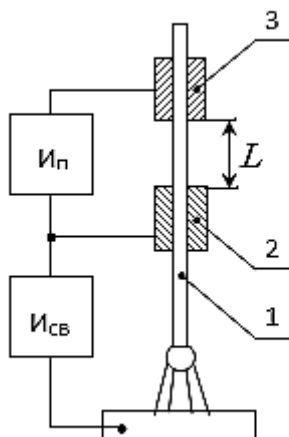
Схема предварительного подогрева проволоки в процессе сварки.
